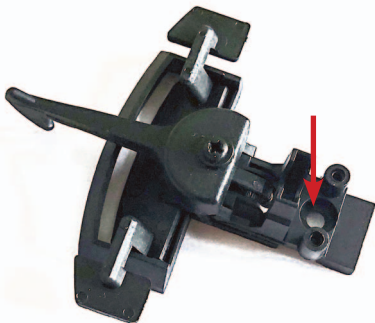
Montage der Entkuppelmechanik an der Kuppungsaufnahme
